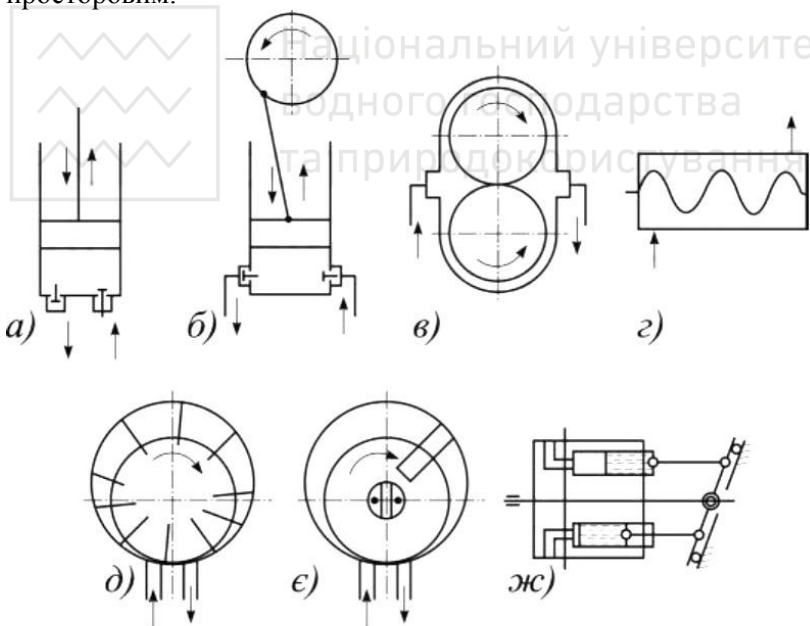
Схеми об'ємних гідромашин: а - поршневий насос; б - поршневий вальний насос; в - плоско-коловоротний (шестеренний); г - гвинтова; д - роторно-пластинчаста; е -
